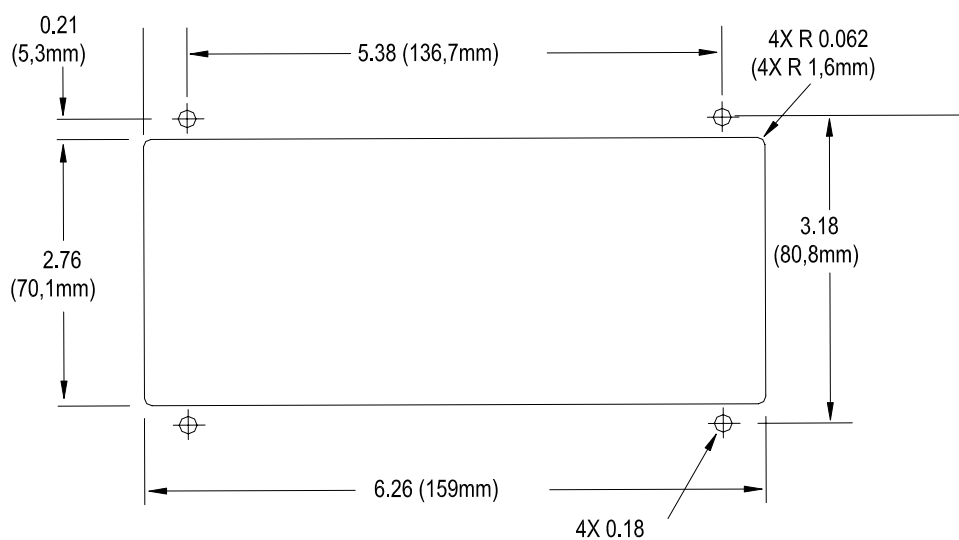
MAQUETTE D'INSTALLATION DU TERMINAL PANTHER MONTAGE SUR TABLEAU
